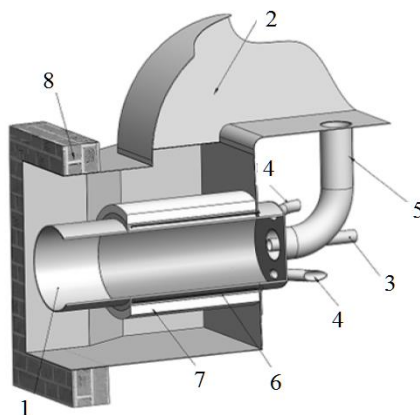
Эскиз универсального горелочного устройства: 1—реакционная труба; 2—короб подвода вторичного воздуха; 3 – подвод пыли высокой концентрации (ПВК); 4 – патрубок тангенциальный подачи первичного воздуха; 5 – патрубок осевой подачи первичного воздуха; 6 – система нагрева; 7 – тепловая изоляция; 8 – амбразура котла.
